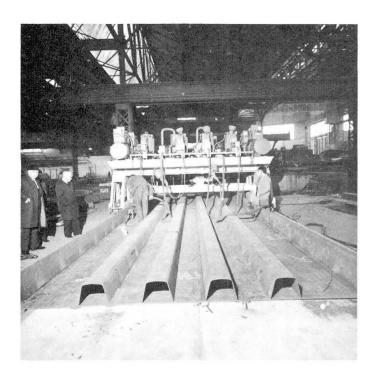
Portique de positionnement des longerons de la dalle orthotrope
